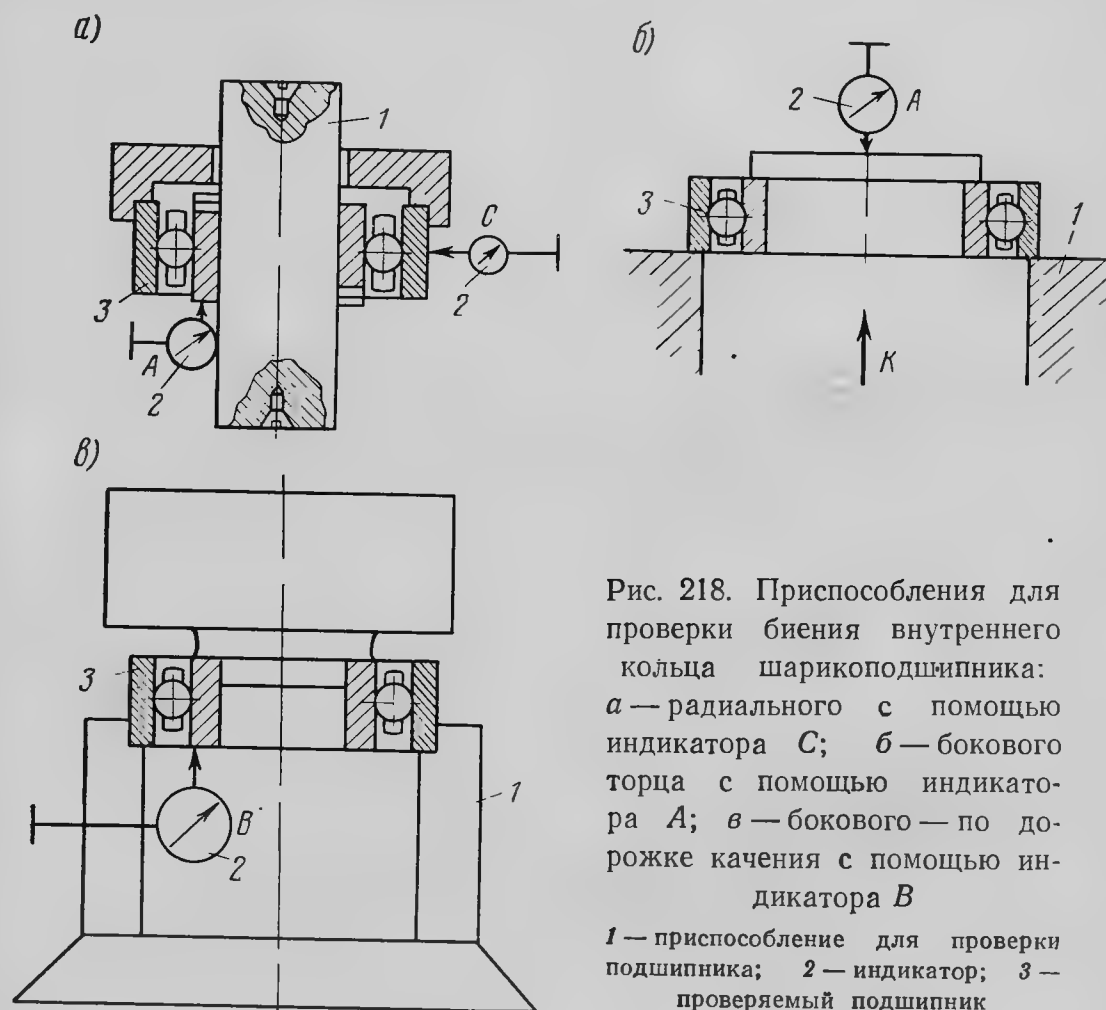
Приспособления для проверки биения внутреннего кольца шарикоподшипника: а — радиального с помощью индикатора С; б — бокового торца с помощью индикатора А; в — бокового — по дорожке качения с помощью индикатора В
